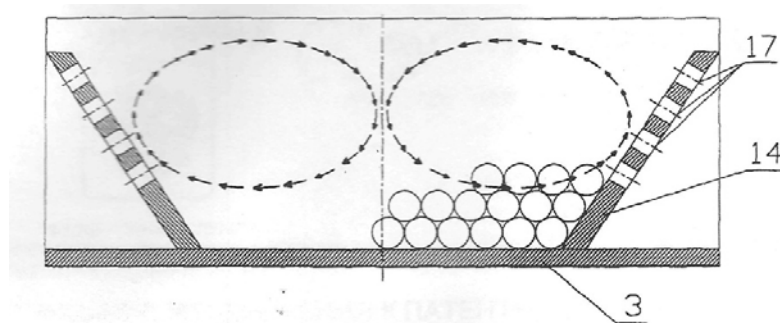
корпус цилиндрической емкости с камерами и мелющими телами;
